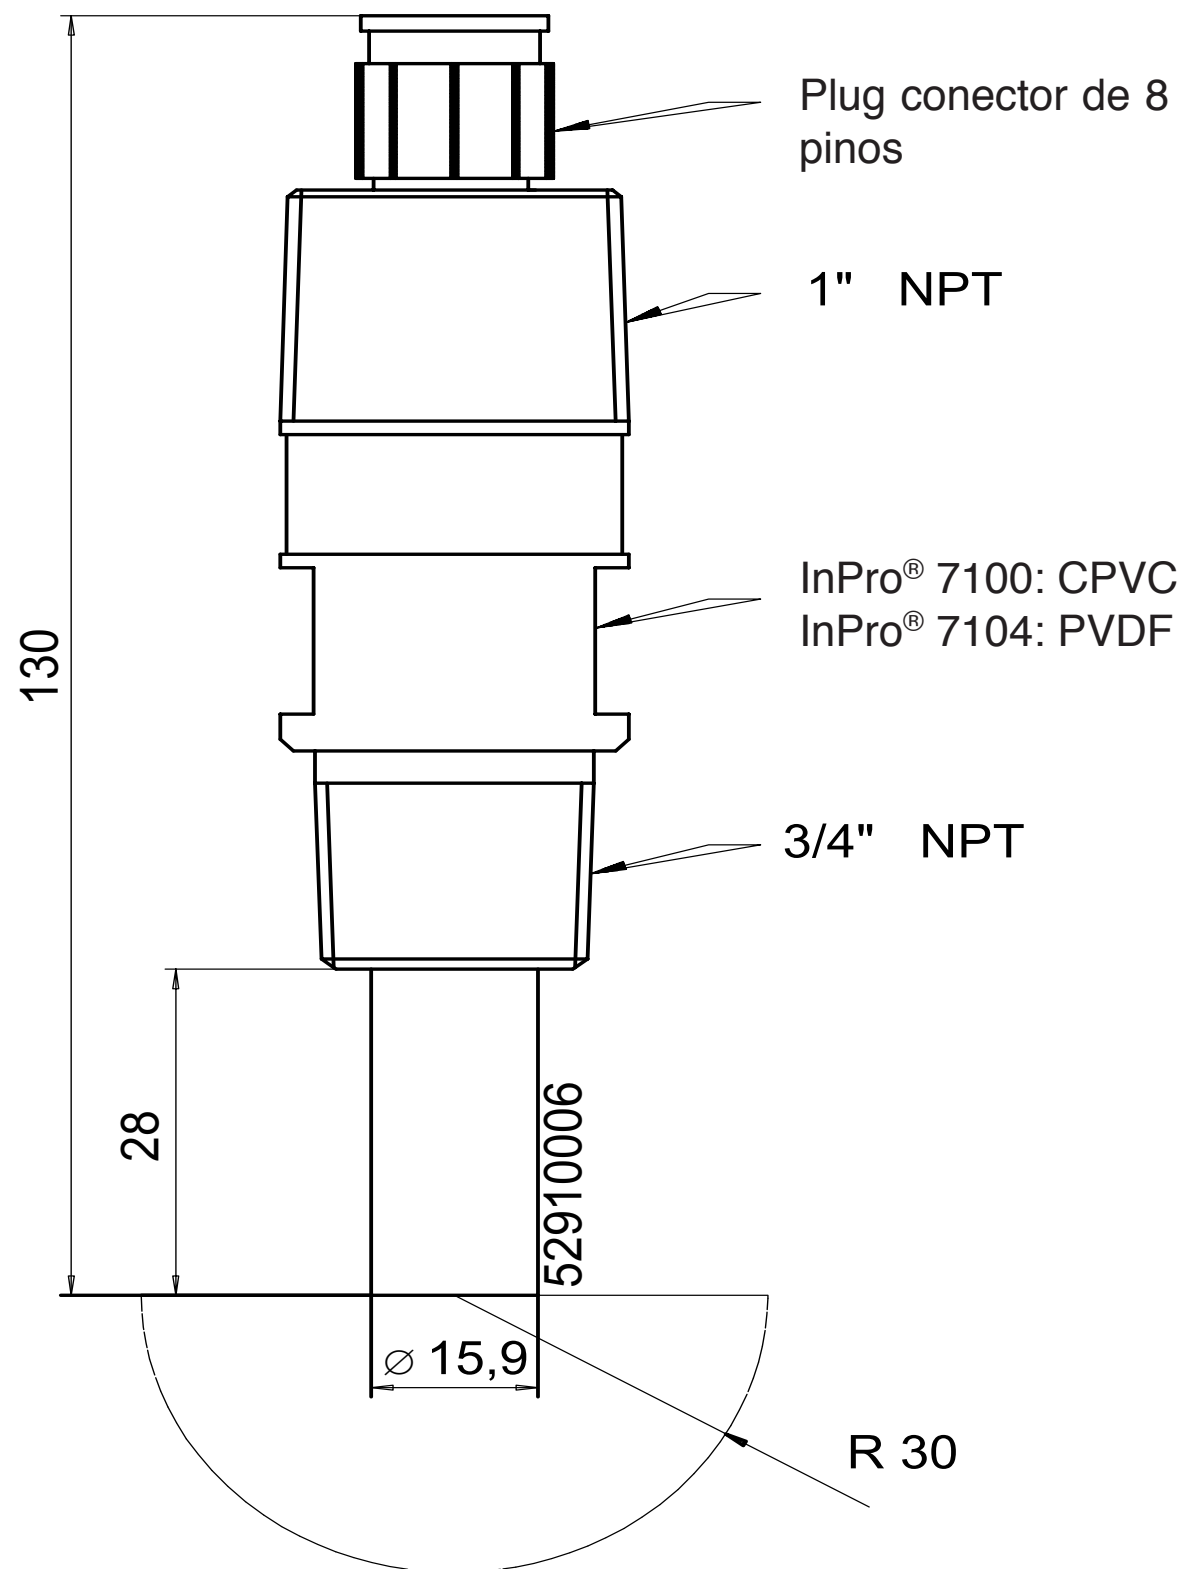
Desenho das dimensões do InPro[®] 7100/7104 com célula com 4 eletrodos
